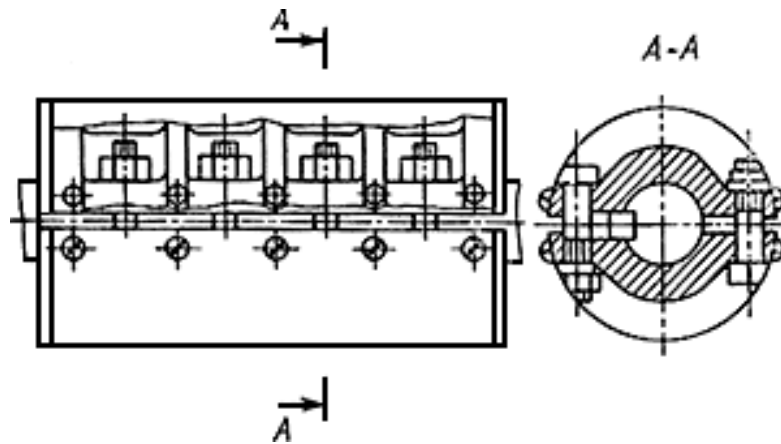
Конструкція поздовжньо-збірної муфти
